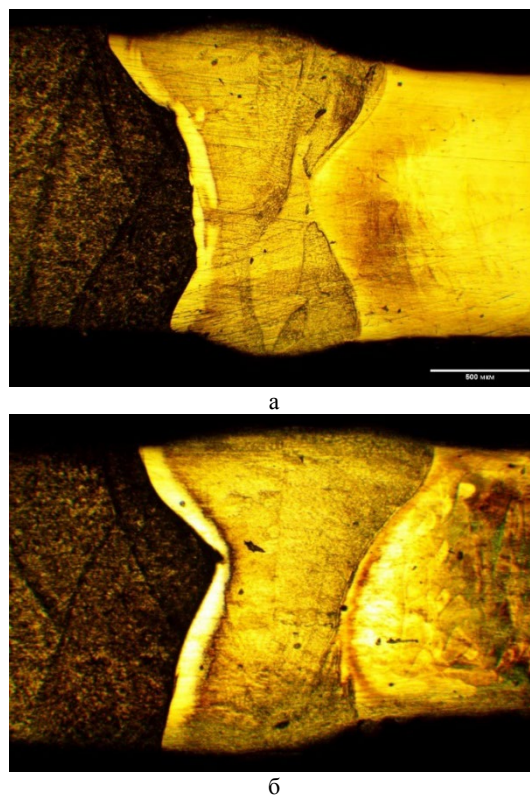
Поперечное сечение сварного шва при смещении луча на заготовку 12X18H10T: а - 0,25 мм; а - 0,5 мм
